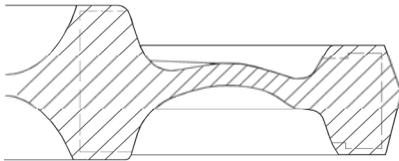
Готовая поковка локомотивного центра. (Powell-Brett)
